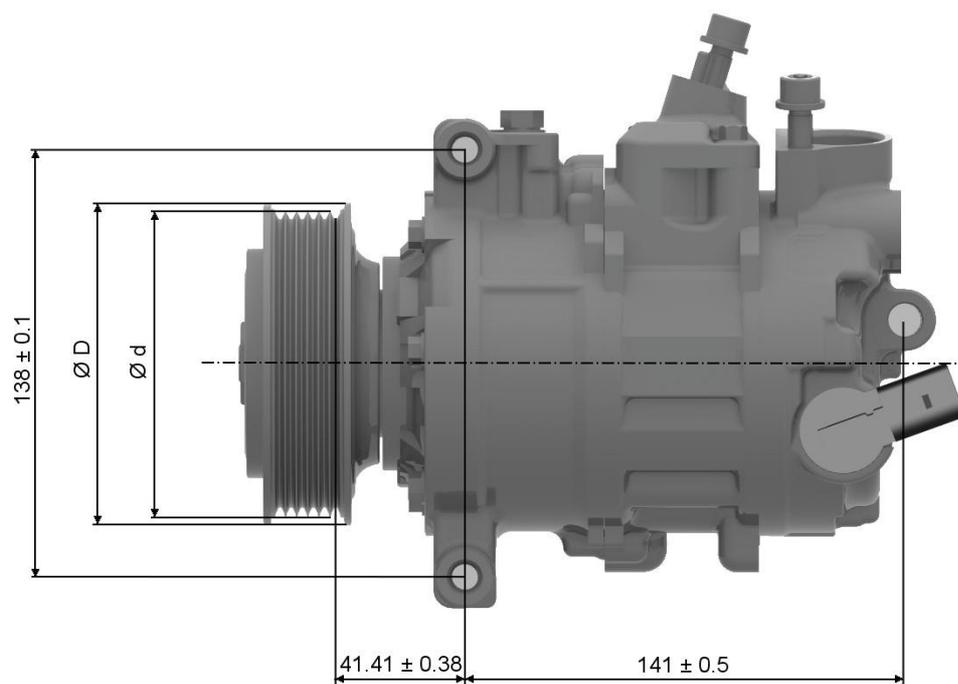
Размеры компрессора климатической установки, диаметр шкива 110 мм (вид сбоку).
